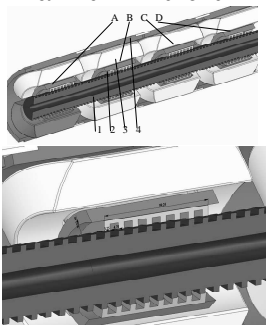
Конструкция двигателя: 1 – ротор, 2 – полюса статора, 3 – катушки фаз, 4 – корпус
